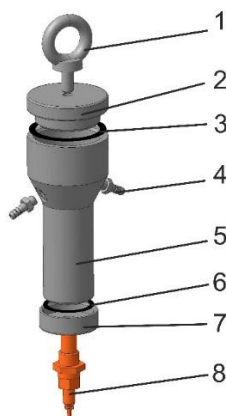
Разрабатываемая конструкция прибора для проверки герметичности соединений
